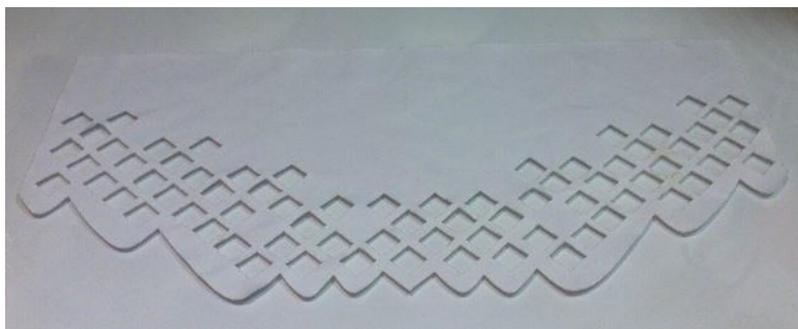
Teste de corte vazado em neoprene alternativo azul
